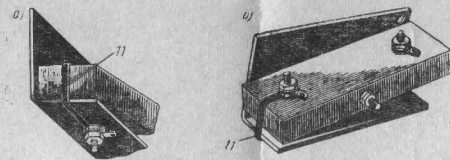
Крепление резины к контактору [б] и уголку [а]
